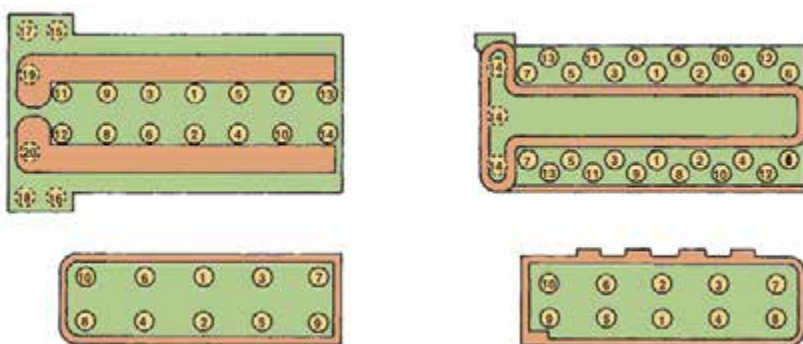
Примеры последовательности затяжки крепежа головки цилиндров двигателей различных конструкций; источник: *Pearson Education, Inc.
